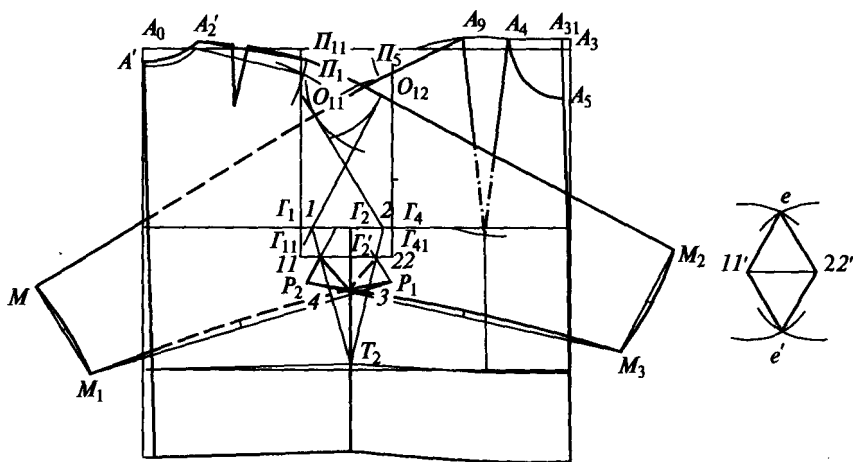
Чертеж конструкции изделия с цельнокроеными рукавами на углубленной пройме с ромбовидной ластовицей
